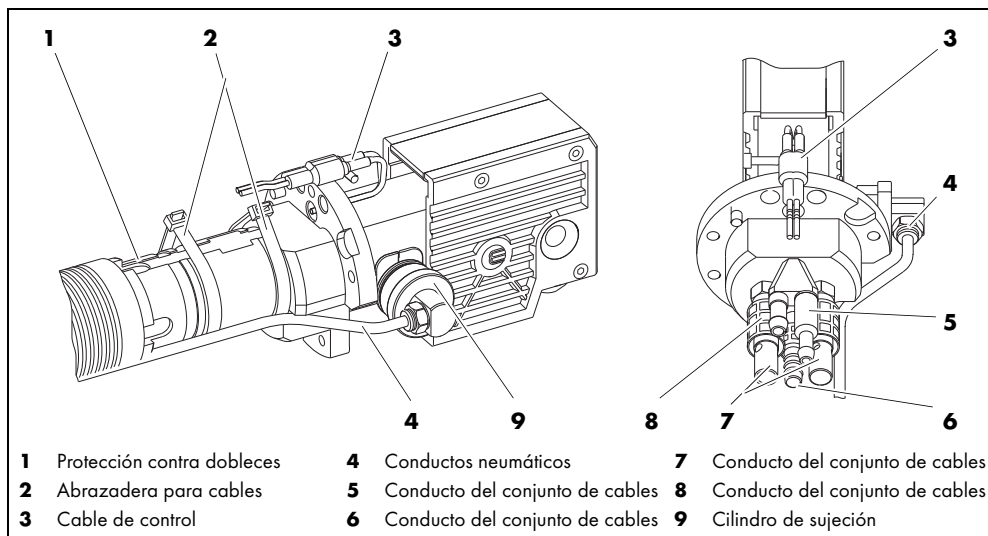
Montar el conjunto de cables de ROBO WH
